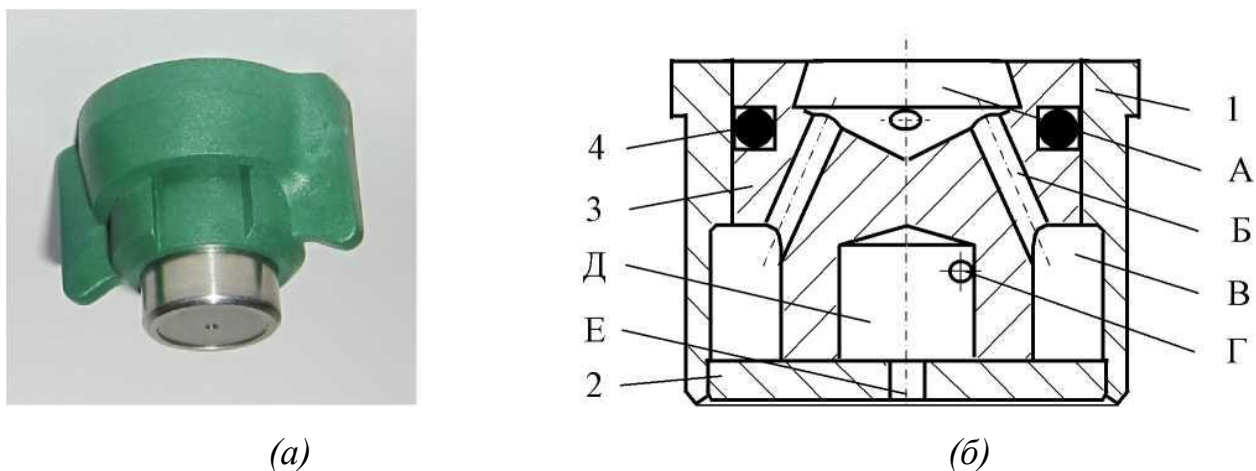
Загальний вигляд (а) і конструктивна схема (б) відцентрового розпилювача: А – розподільник; Б – канали; В – кільцевий колектор; Г – вхідні канали; Д – камера закручування; Е – сопловий отвір; 1 – корпус; 2 - сопло; 3 – завихрювач; 4 - гумове кільце.
